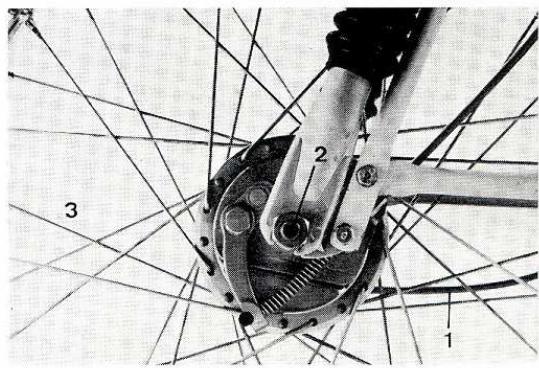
DEMONTAGE DE LA ROUE AVANT.
